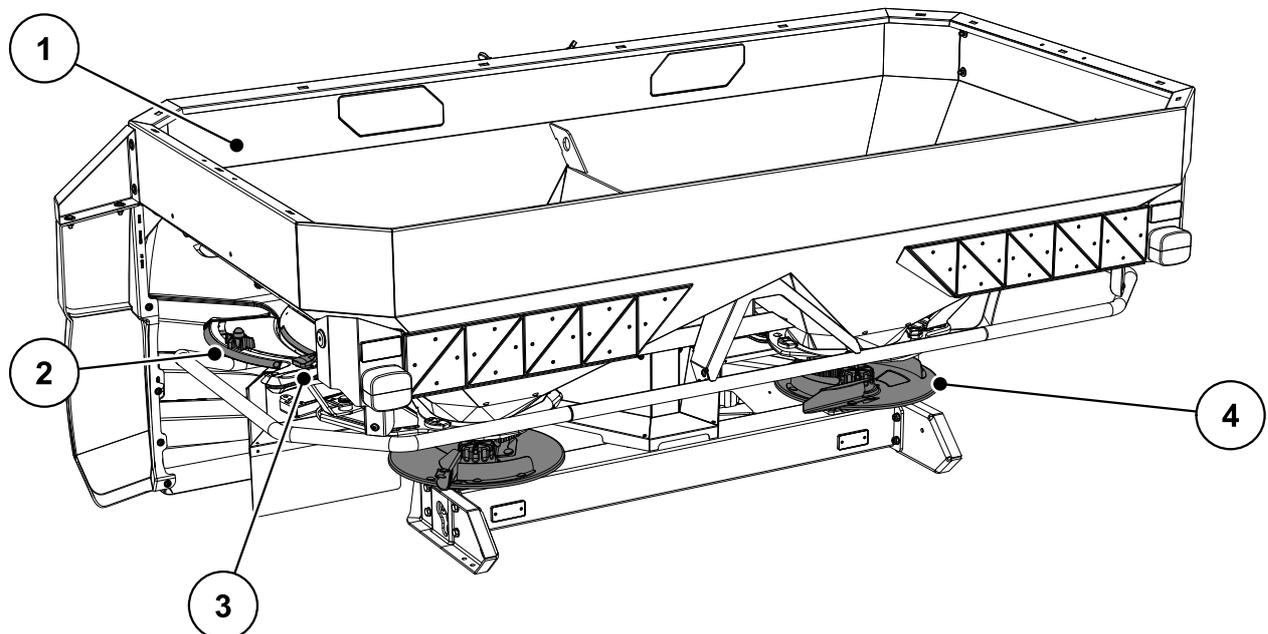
Aperçu des modules : Exemple AXIS 30.1 - vue arrière
